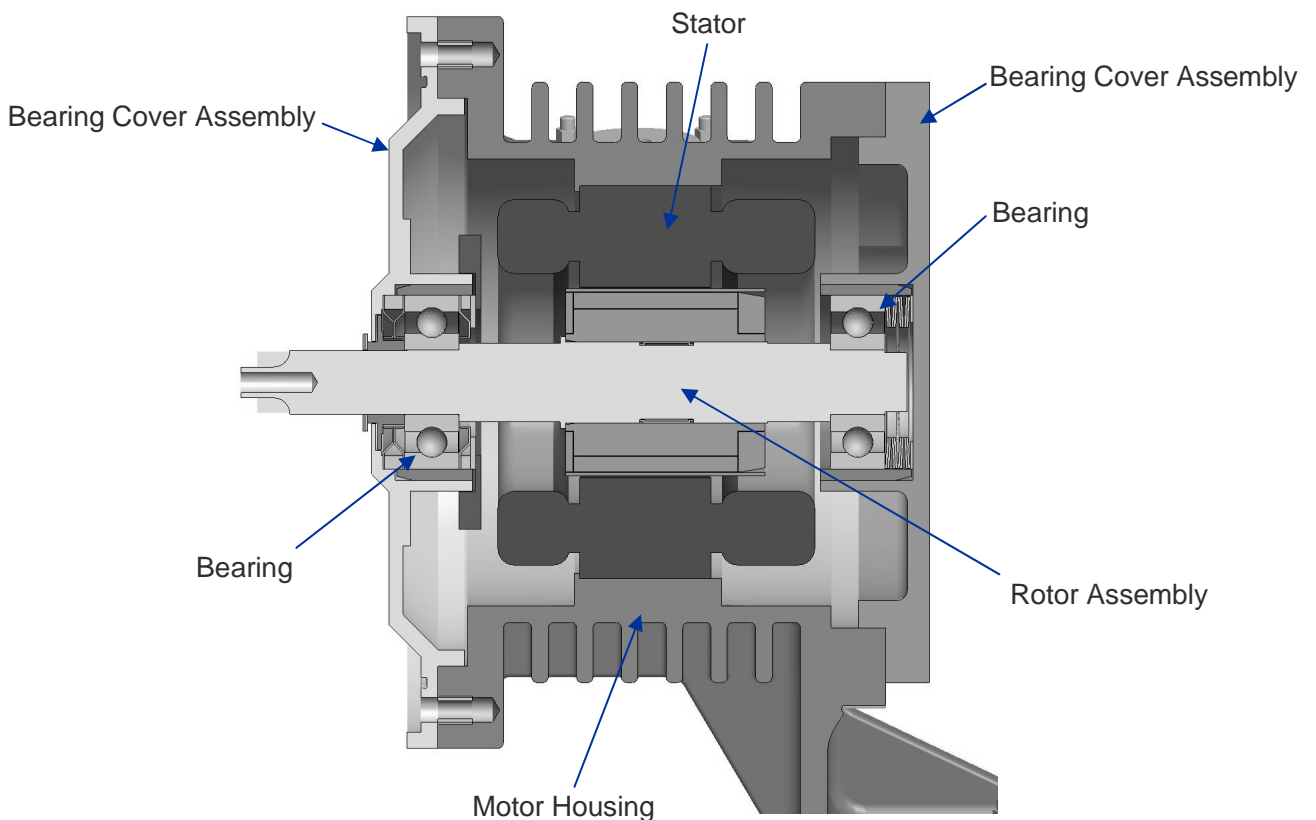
Vakuum-Generator Motor - Querschnitt
